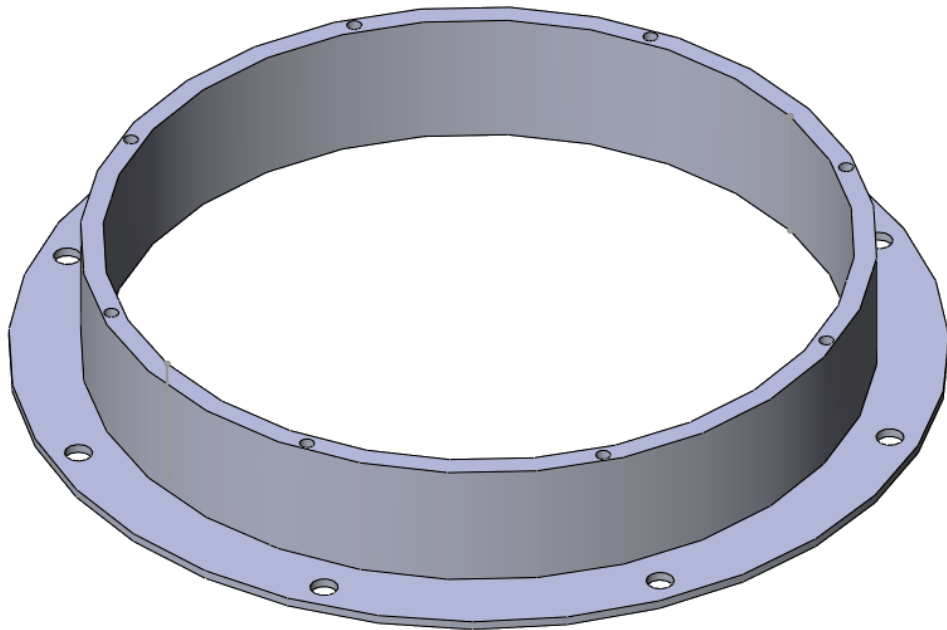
Верхня частина корпусу підшипникового вузла після підвищення вагової ефективності
